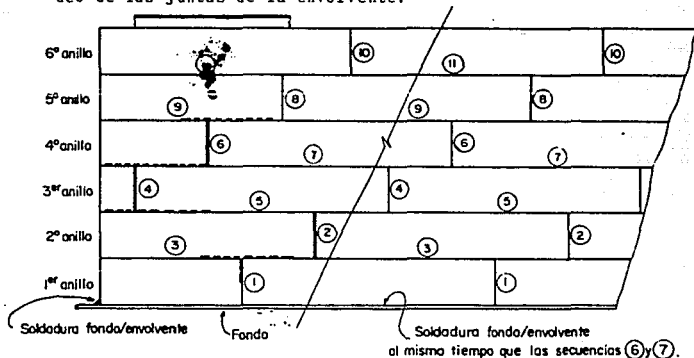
SECUENCIA DE SOLDADURA EN LA ENVOLVENTE TRAZOS PREVIOS AL MONTAJE DEL PRIMER ANILLO.
